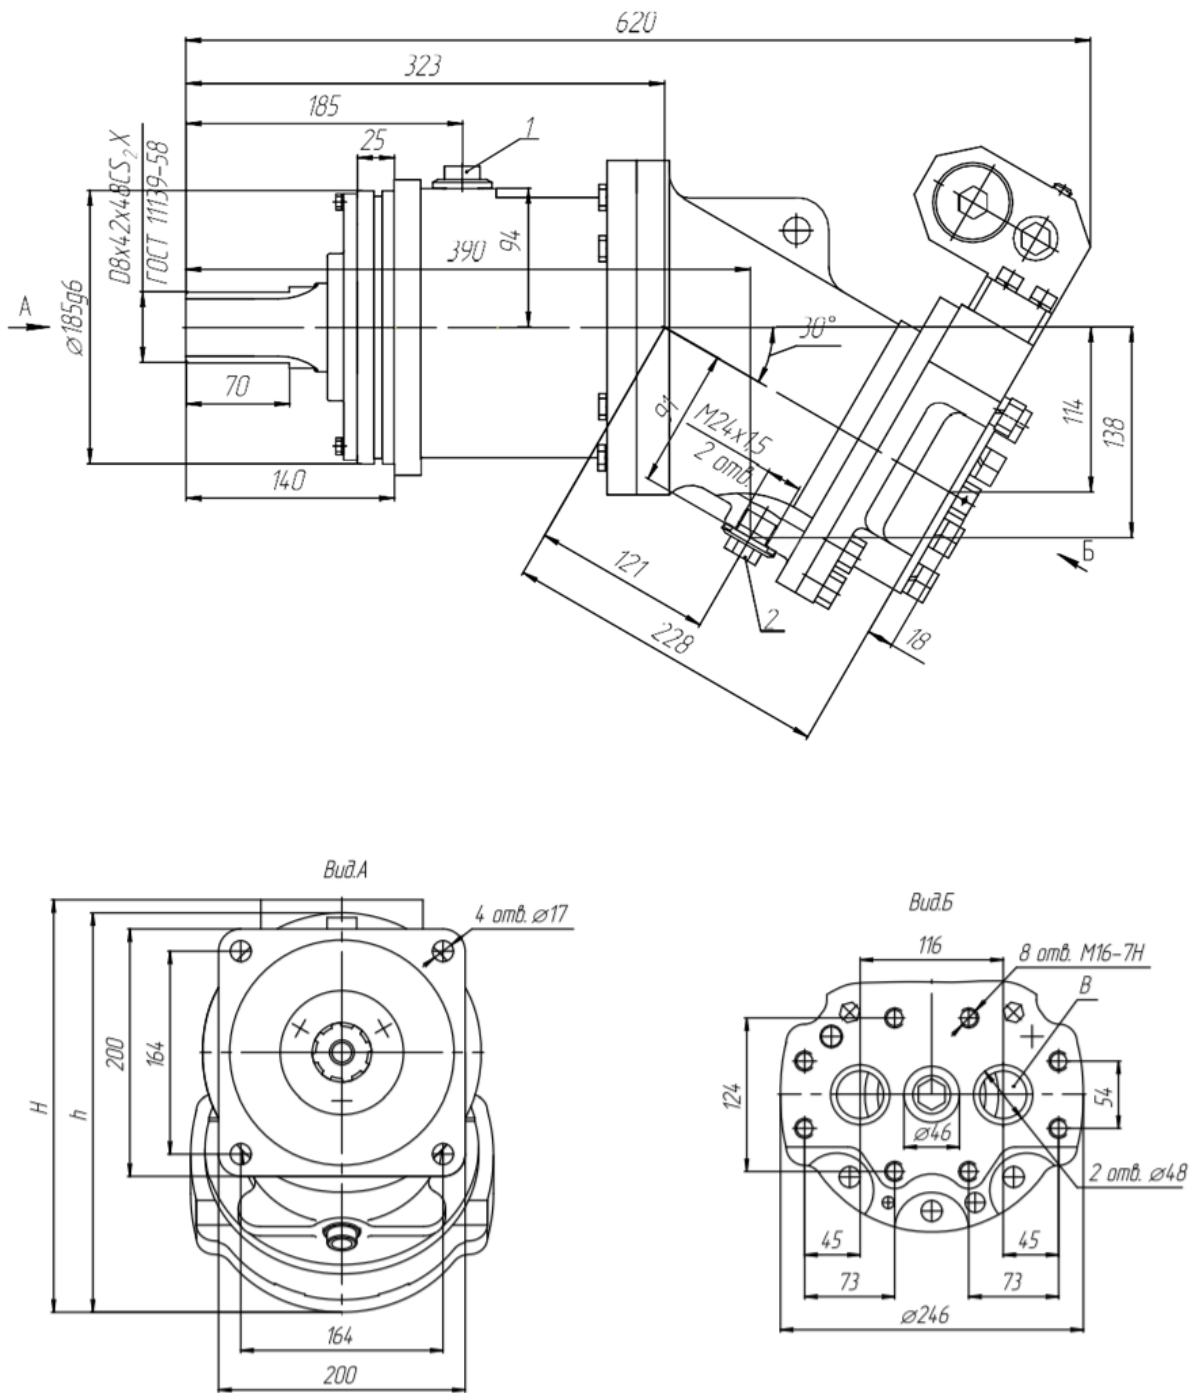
Габаритные и присоединительные размеры насос-мотора
